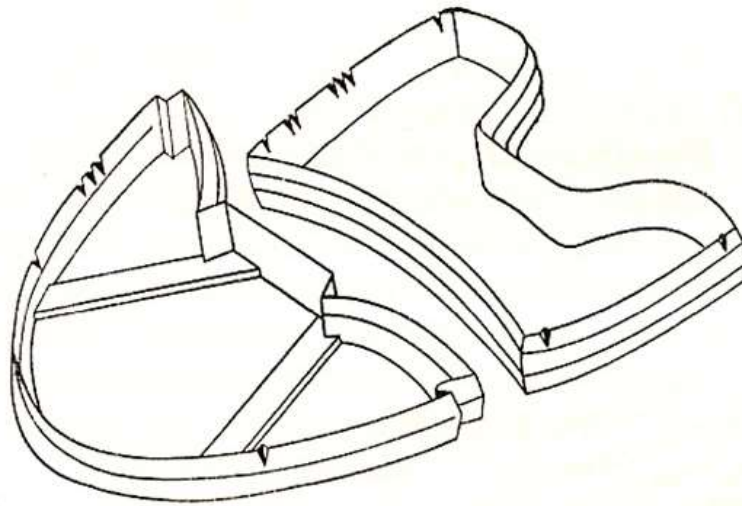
Різаки для вирубування деталей верху взуття
